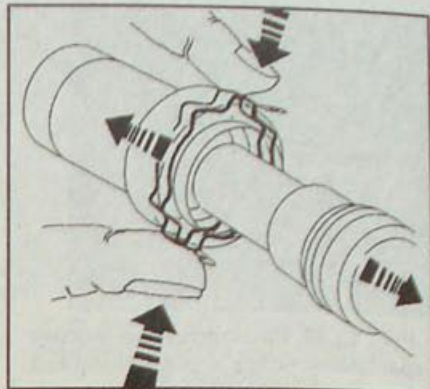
Направление нажатия деформируемого кольца осевой блокировки при разъединении быстроразъемного соединения отводящего и подводящего шлангов отопителя на автомобилях с двигателями F3R
